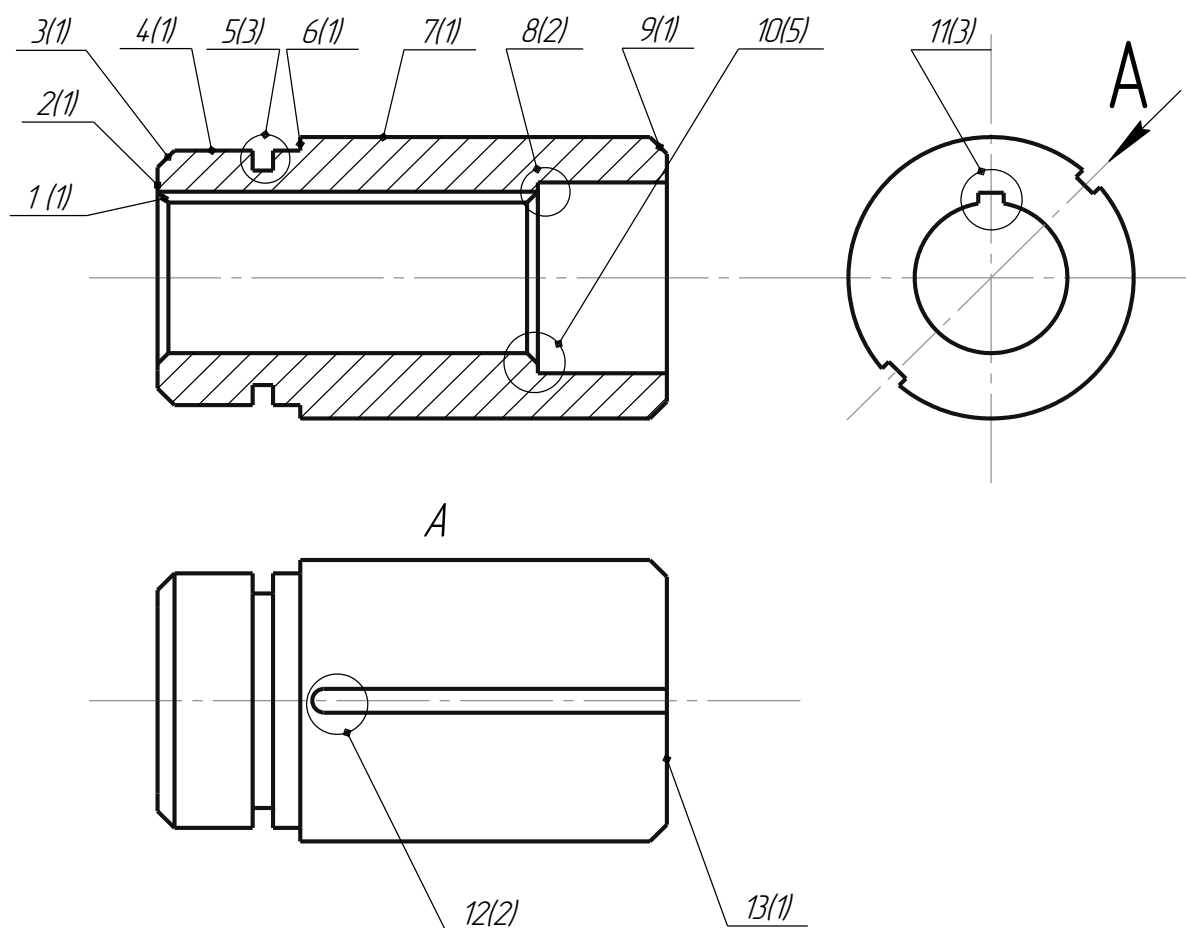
Елементи переходника: 1, 3, 9 – фаска; 2, 13 – торець; 4, 7 – ступінчаста циліндрична поверхня; 5 – канавка; 6 – заплечик; 8 – виточка; 10 – ступінчастий отвір; 11 – шпонковий паз наскрізний; 12 – шпонковий паз напіввідкритий. В дужках помічена кількість поверхонь, що входять в елемент
